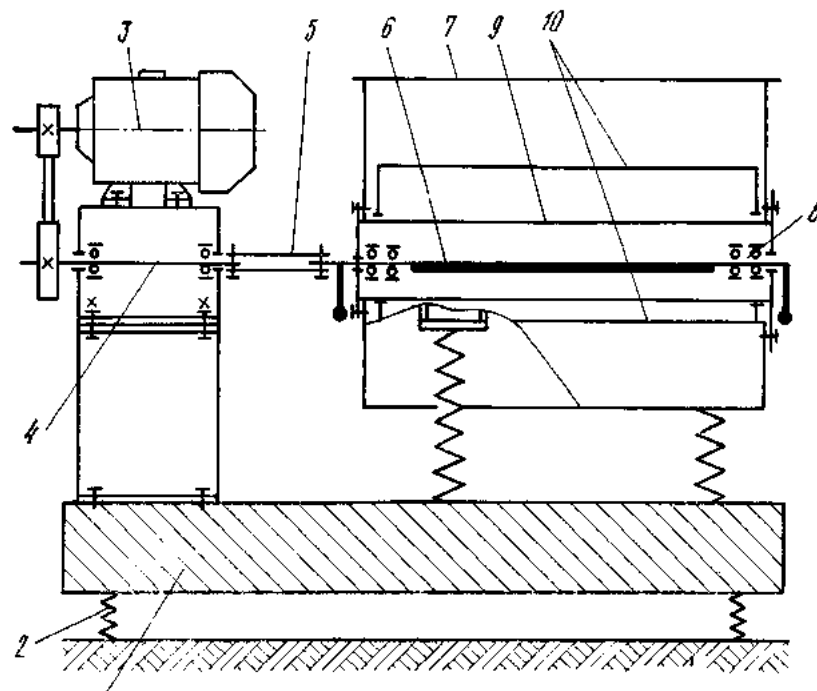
Вібраційна машина з робочим тілом: 1 – основа;
